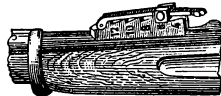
Ступенчато-рамочный открытый прицел русской военной винтовки образца 1891 г.
